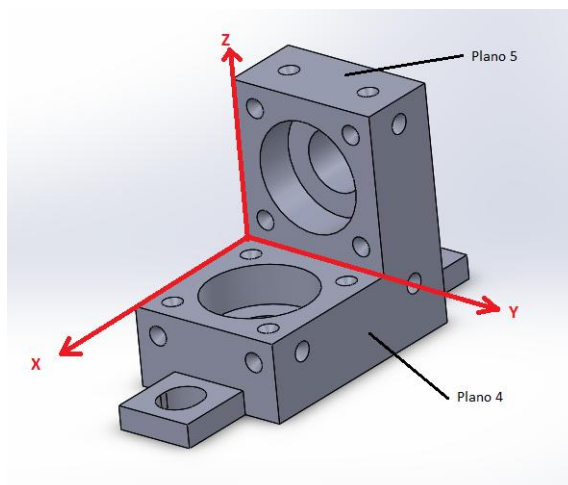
PLANOS 4 Y 5 EN PIEZA A
